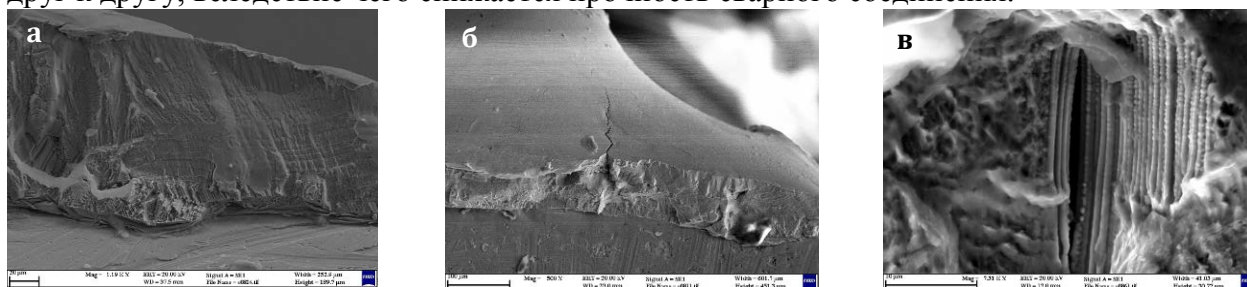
Характерные виды изломов сварных швов
